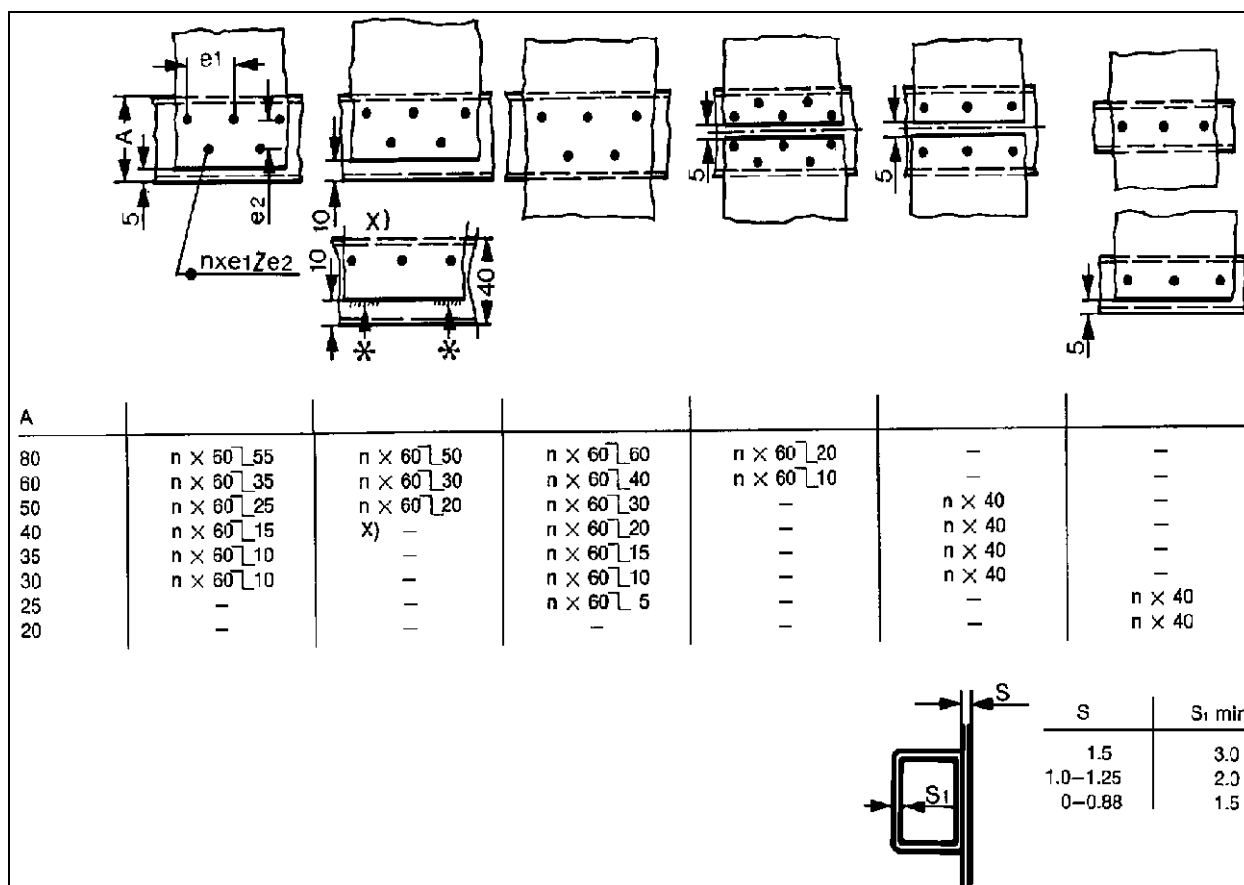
Especificaciones para soldadura eléctrica con puntos por resistencia
